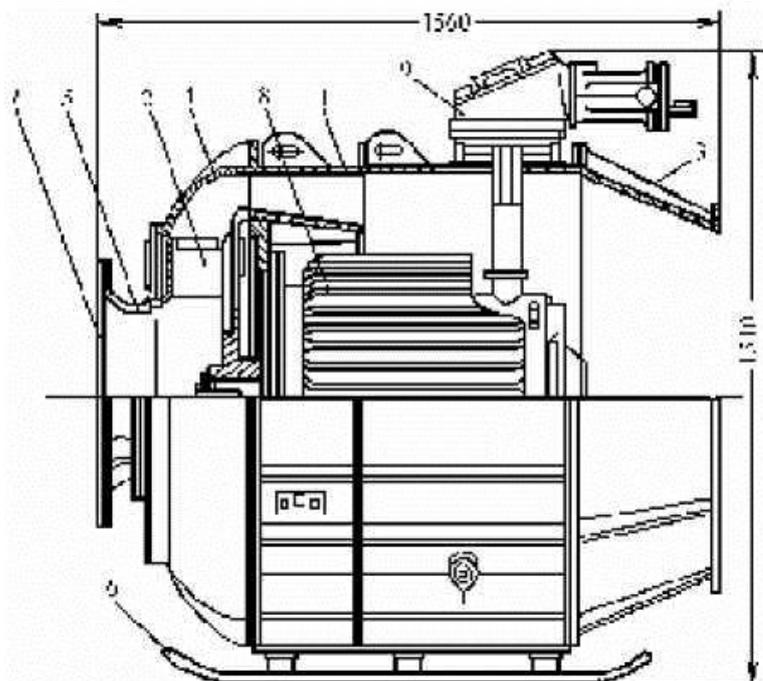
Вентилятор ВЦ-7: 1- кожух; 2 - рабочее колесо; 3 - выходной патрубок; 4 - передняя часть корпуса; 5 - переходник; 6 - салазки; 7 - коллектор; 8 - двигатель; 9 -кабельный ввод
